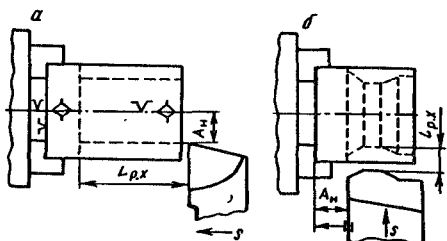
Схемы размерной настройки при токарной обработке:
